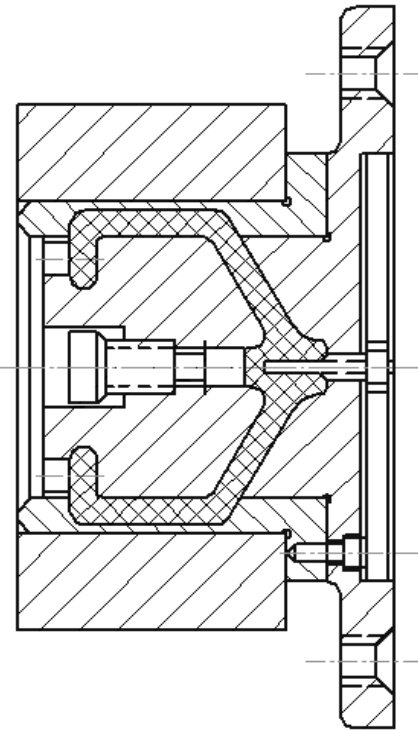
Установка заготовок на розтискній оправці з гідропластом.
